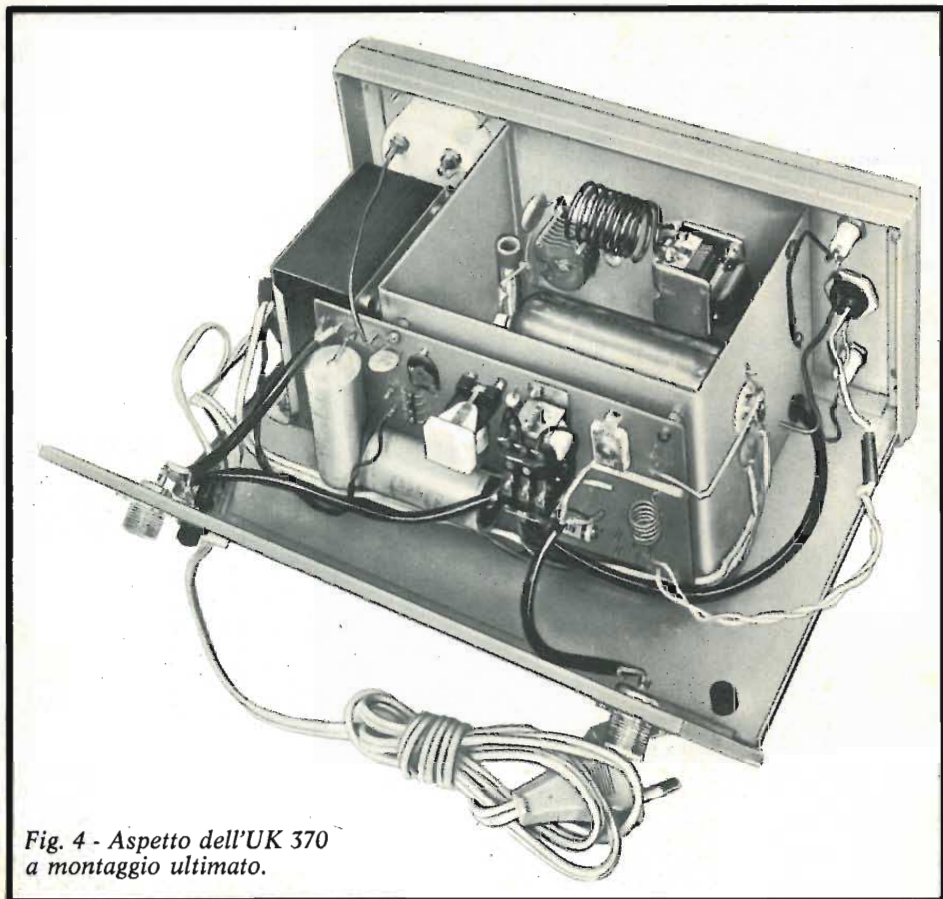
Aspetto dell'UK 370 a montaggio ultimato.
